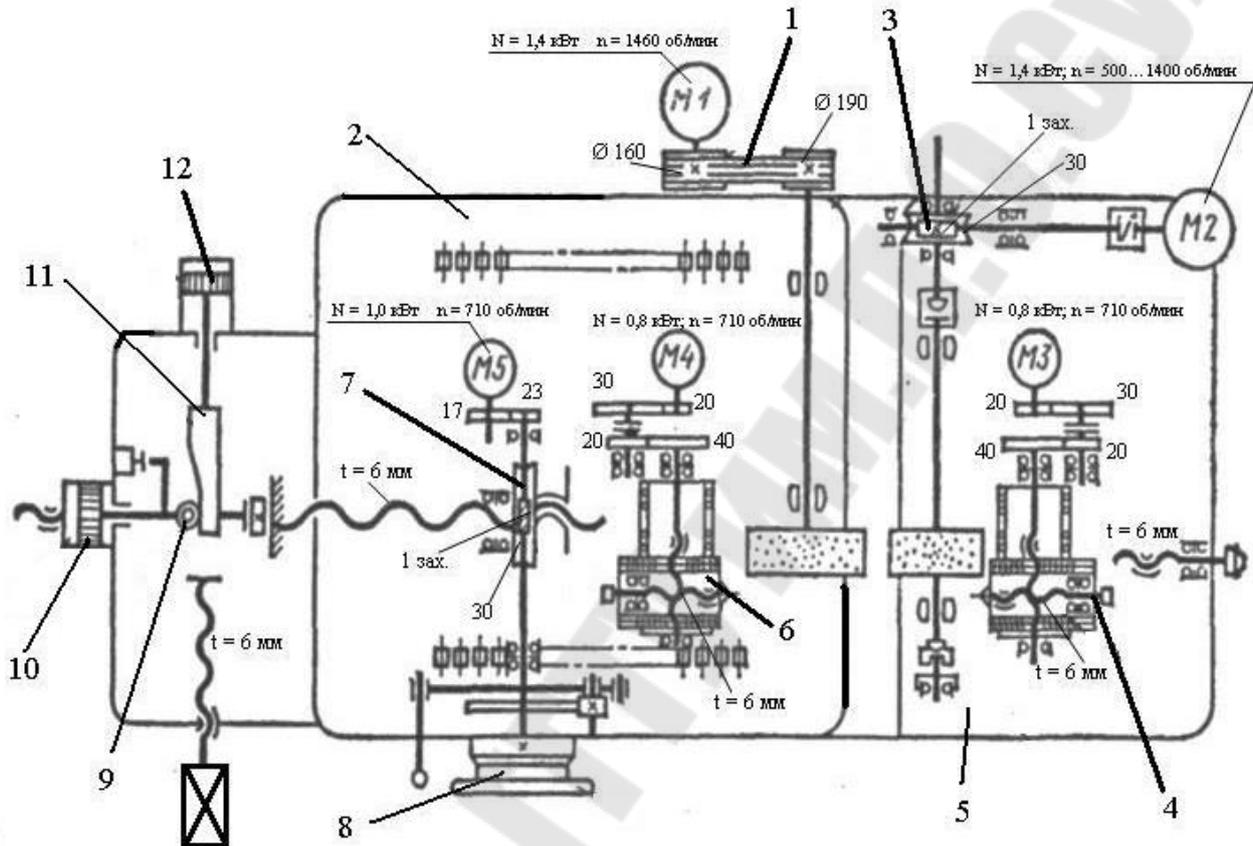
Кинематическая схема круглого бесцентрово-шлифовального станка
